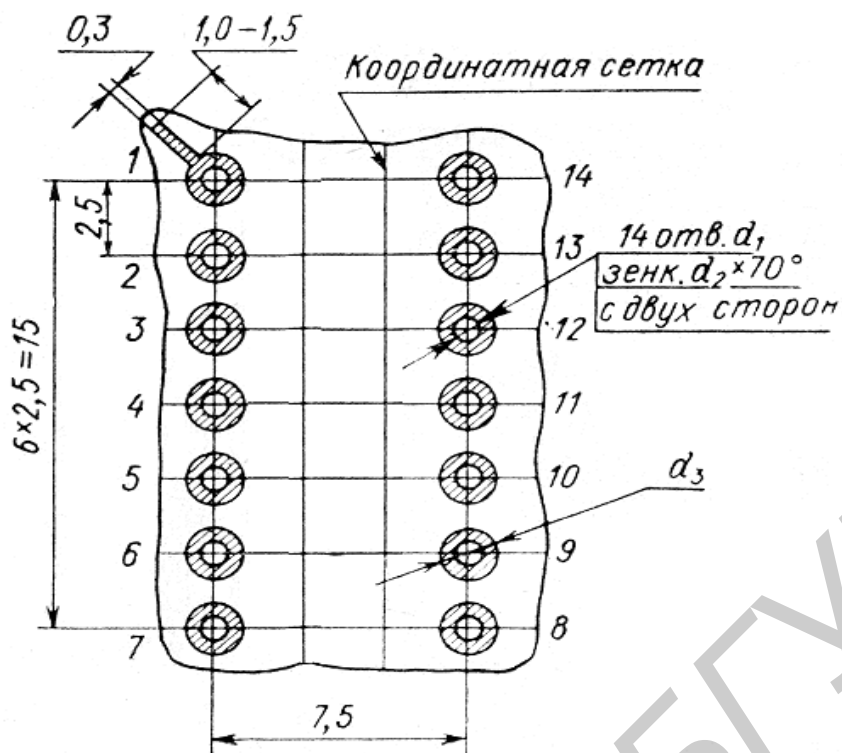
Разметка посадочного места для микросхемы в корпусе типа 2:
